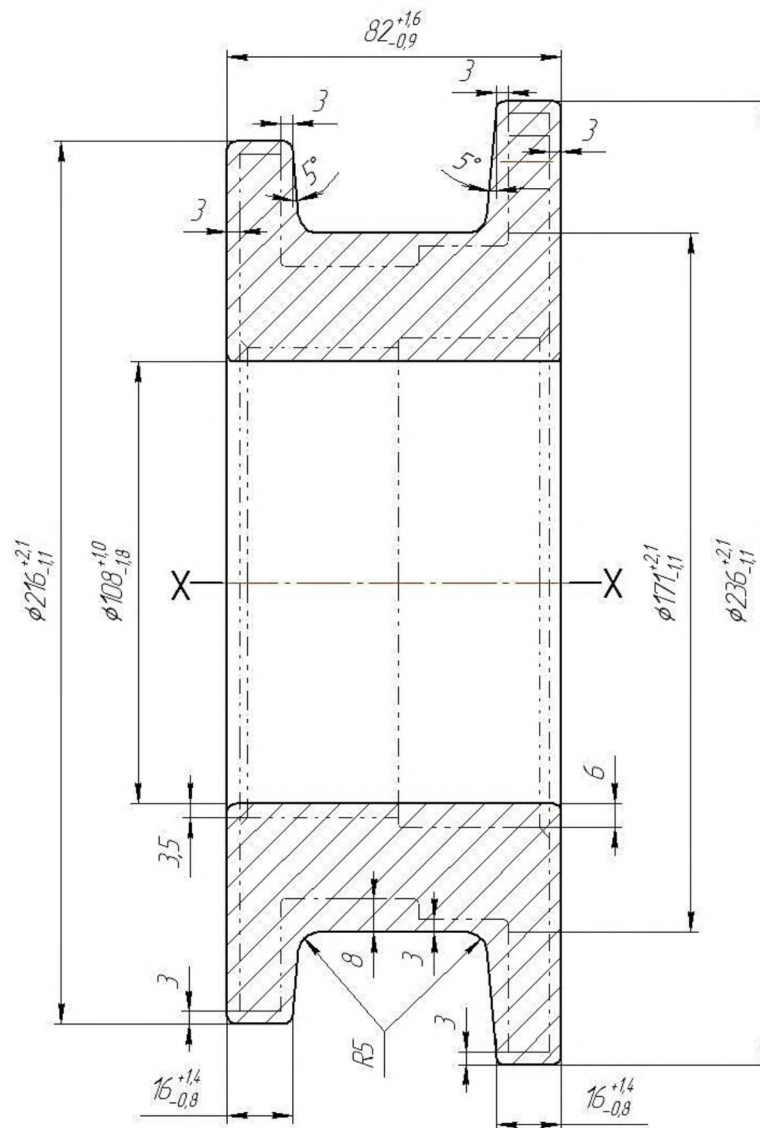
Ескіз заготовки (кування штамповане)
